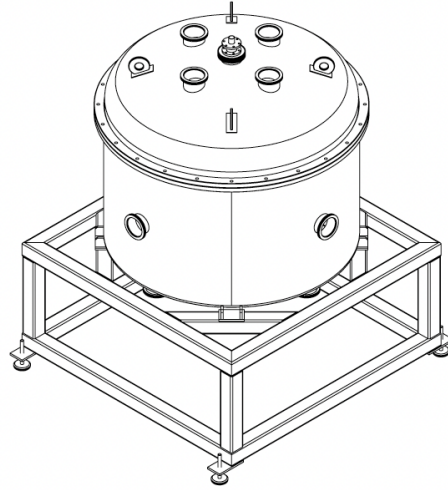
disegno dell'evaporatore del coating wavelength shifter
